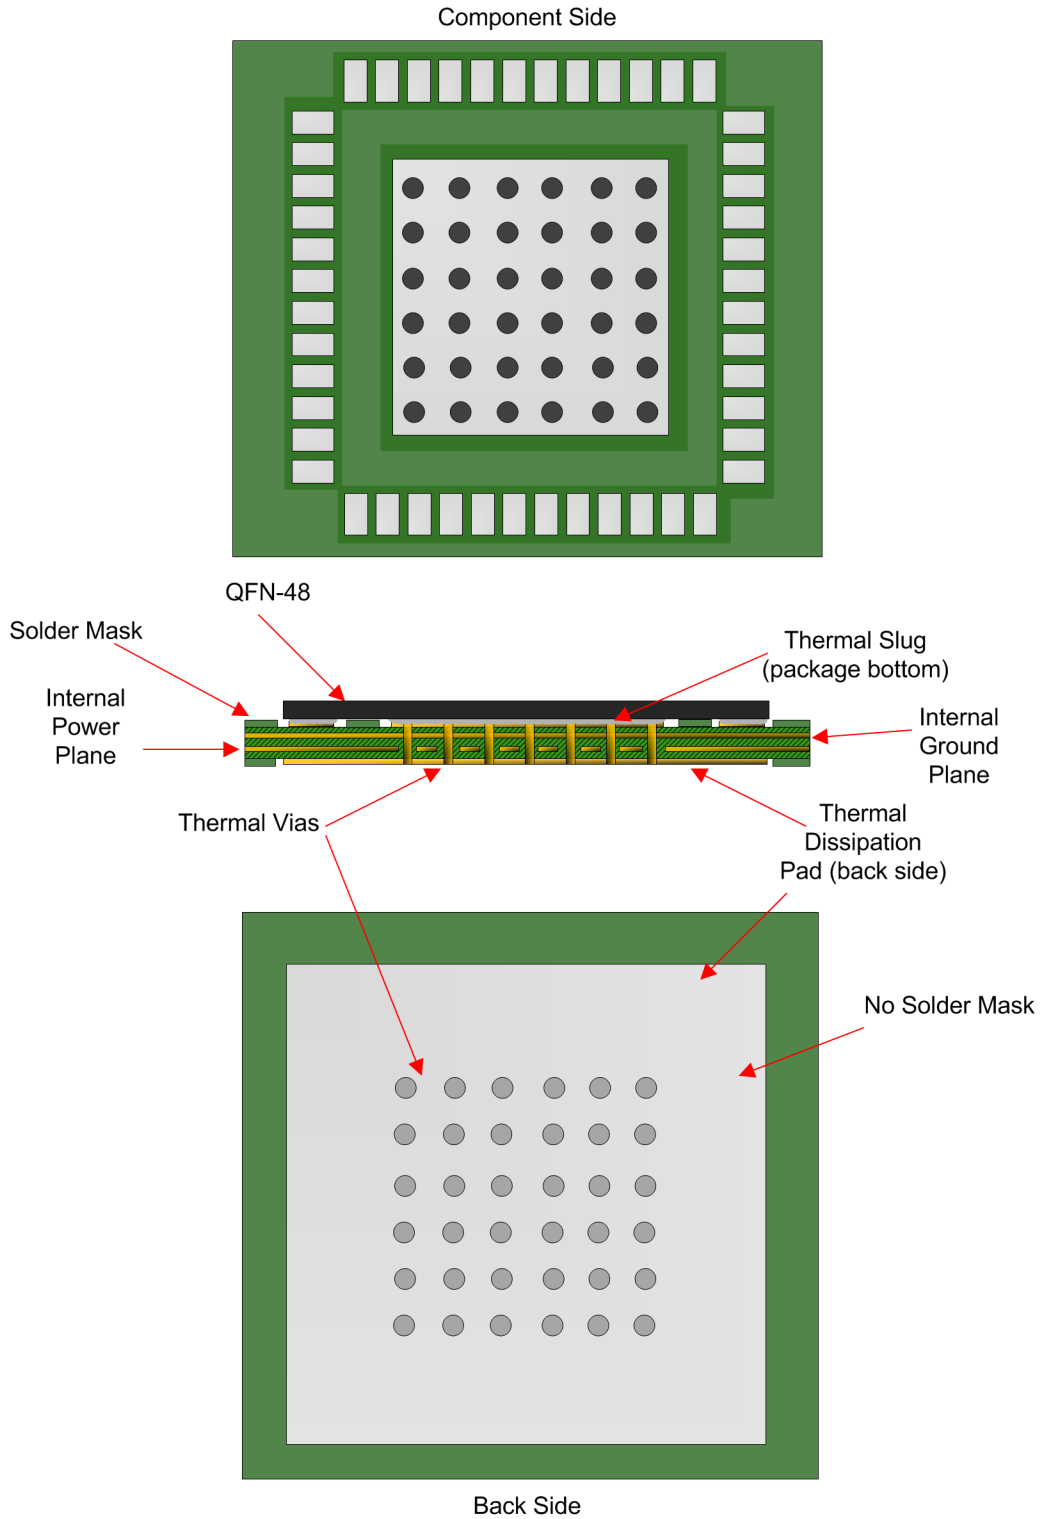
可实现热可靠性的通用 PCB 接地布局 ( 建议 8 层以上 )
